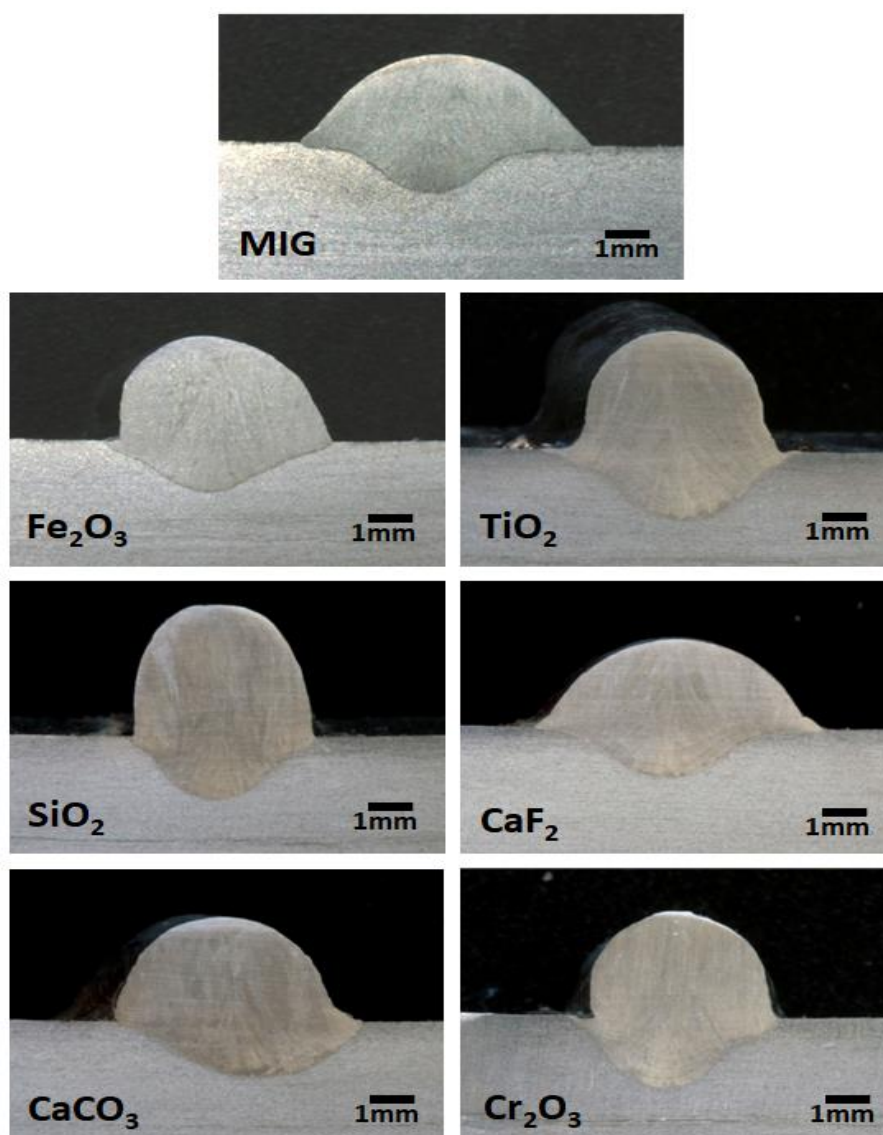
Macrografias de soldas MIG e A-MIG realizadas com parâmetros de soldagem iguais.
